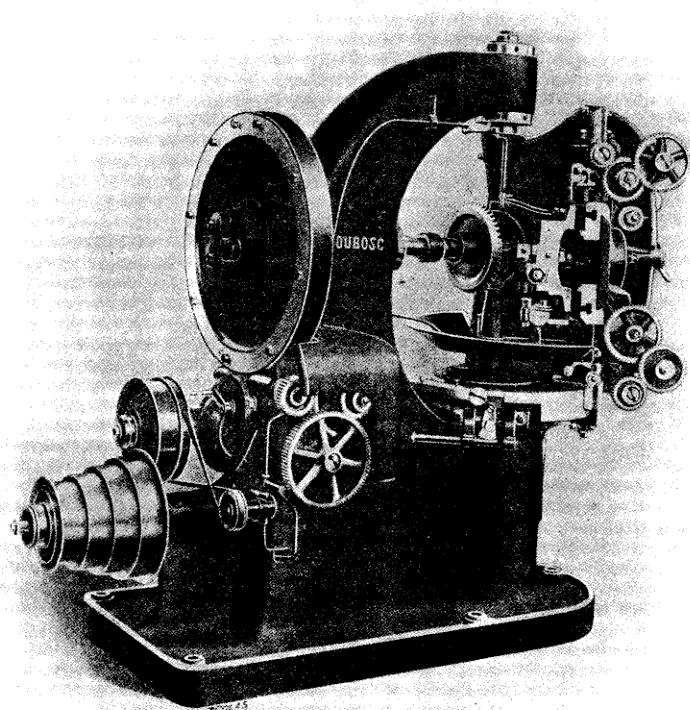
Machine automatique à tailler les engrenages coniques.
